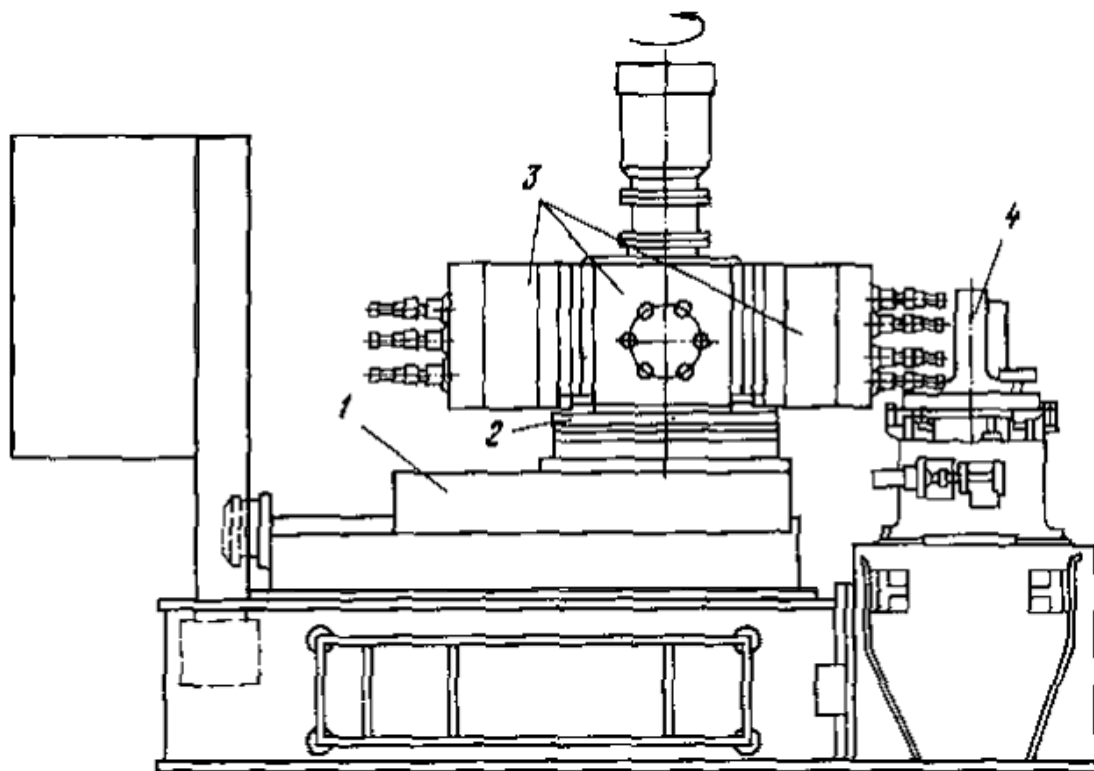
Верстат з поворотними шпиндельними коробками:
